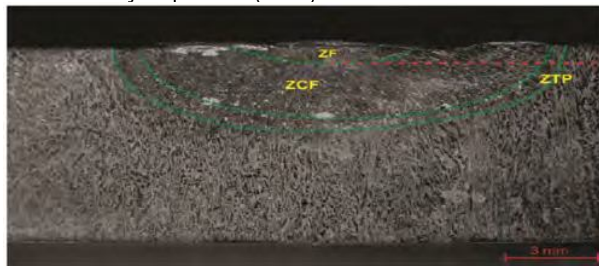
Macrografia da seção transversal do corpo de prova soldado.
